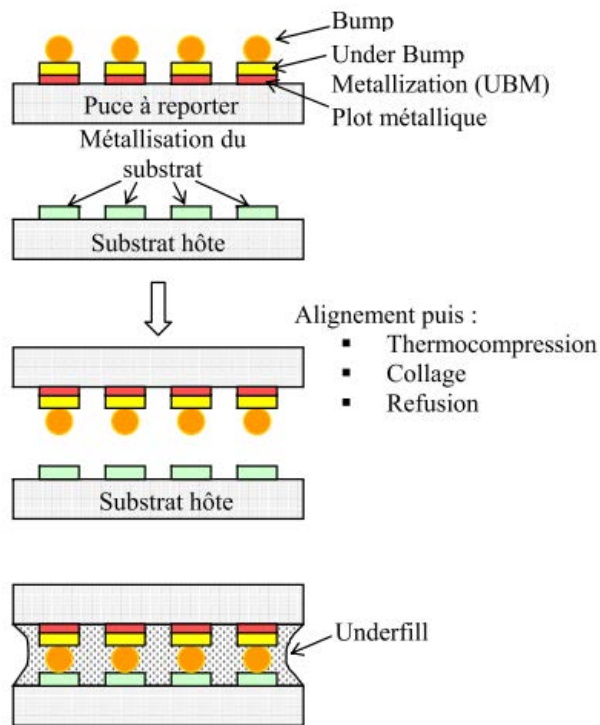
Technique d'assemblage par flip-chip [DaPe06]
